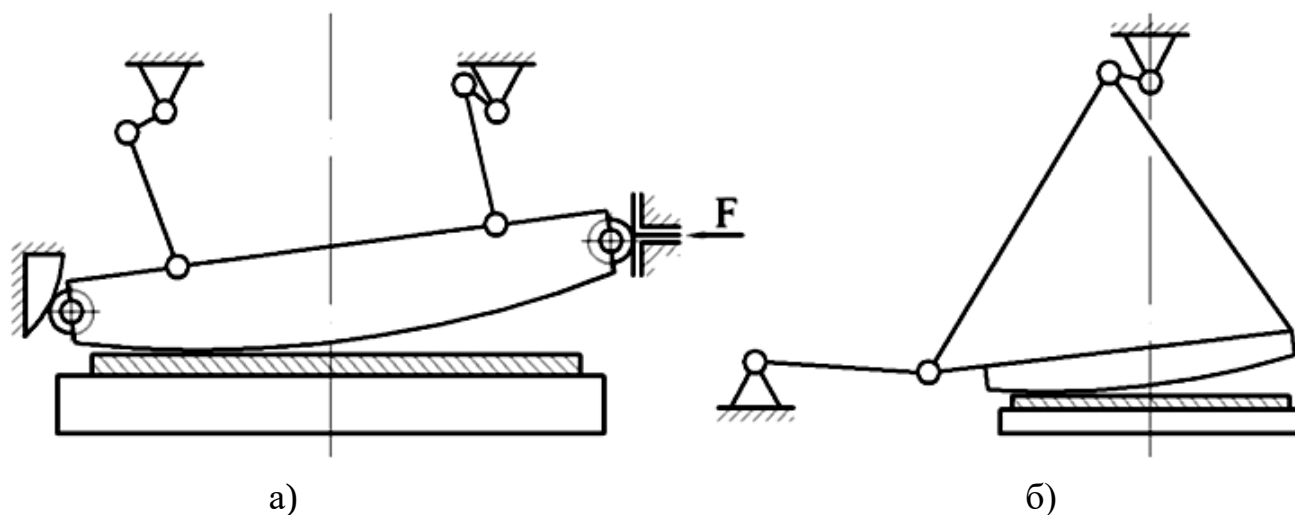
Кінематична схема ножиць з катящимся різом: двохкривошипний (а) і однокривошипний (б)
